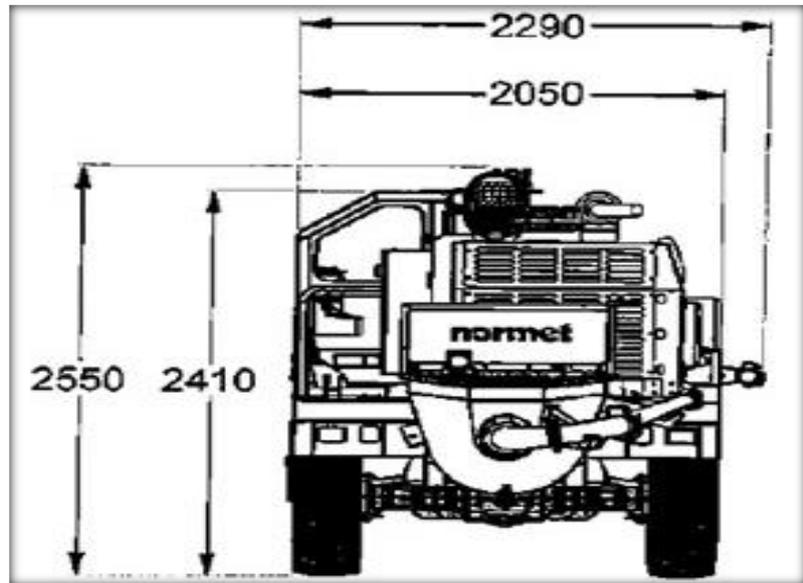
Dimensión de equipo vista trasera Alpha 20.
